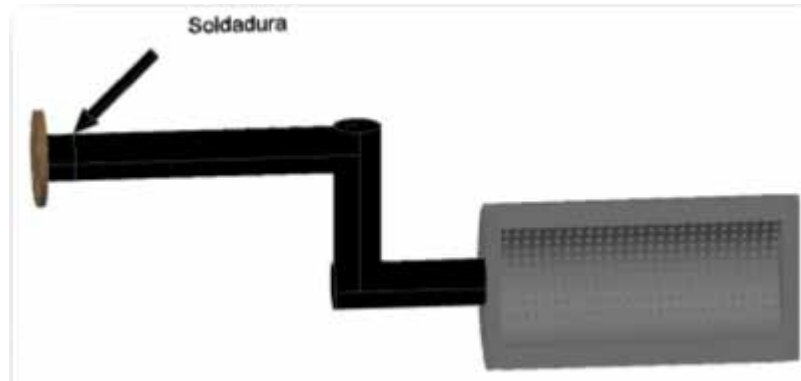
Localización de la soldadura entre la cesta y el brazo
